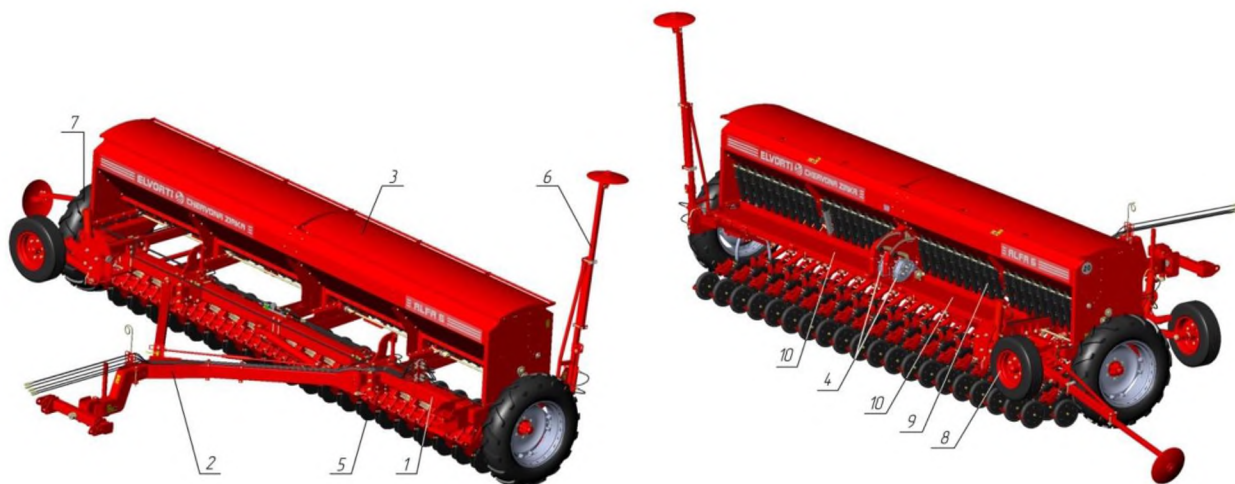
Сівалка ALFA 6 [4]: 1 – рама; 2 – причіпний пристрій; 3 – зерно-туковий бункер; 4 – варіатори; 5 – сошник; 6 – маркер; 7 – опорно-приводне колесо; 8 – колесо для транспортування; 9 – висівний апарат; 10 – підніжна дошка; 11 – ланцюговий загортач
